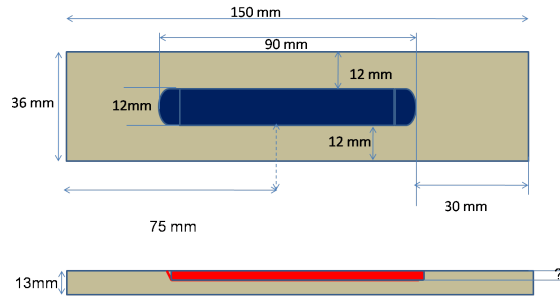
Dimension de la plaque soudée
